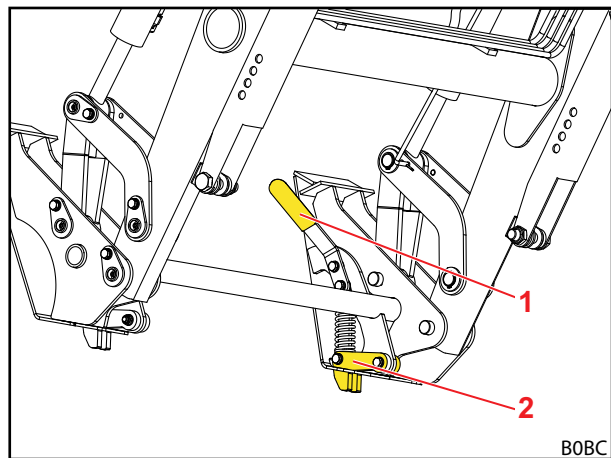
Mechanische Werkzeug-Verriegelung Skid-Steer (verriegelter Zustand ohne Werkzeug)
